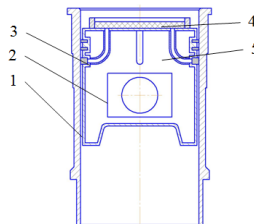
Схема смазывания рабочей поверхности гильзы
